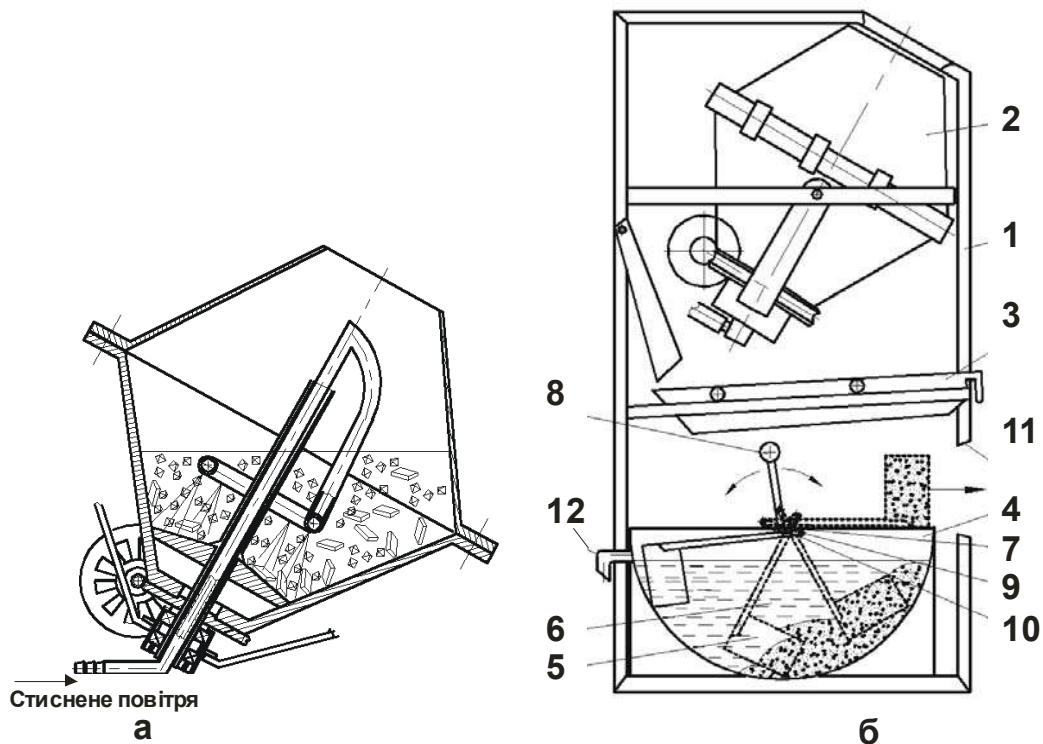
Компоновочна схема пристрою для абразивної обробки затопленими струменями [50]
